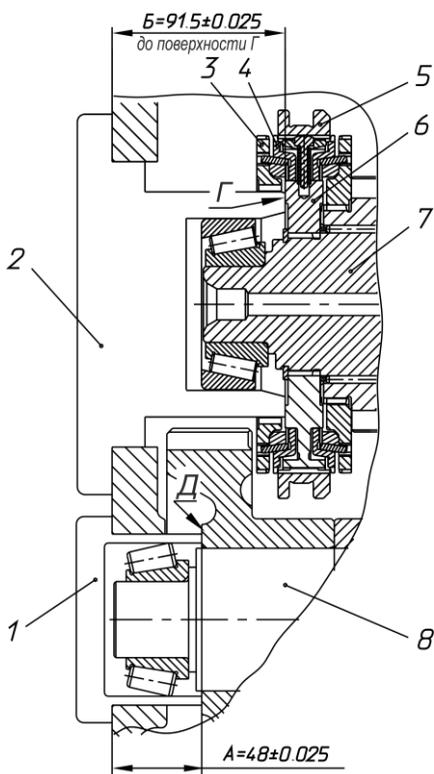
Установка промежуточного и вторичного валов в сборе
